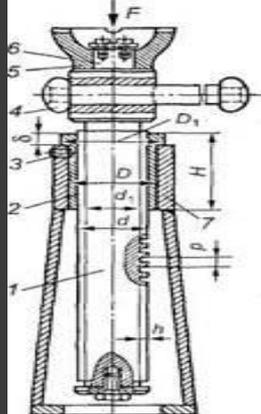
Винтовой домкрат: 1—винт; 2 — гайка; 3 — стопорный винт; 4 — рукоятка; 5 — чашка домкрата; 6— шип, 7 — корпус
